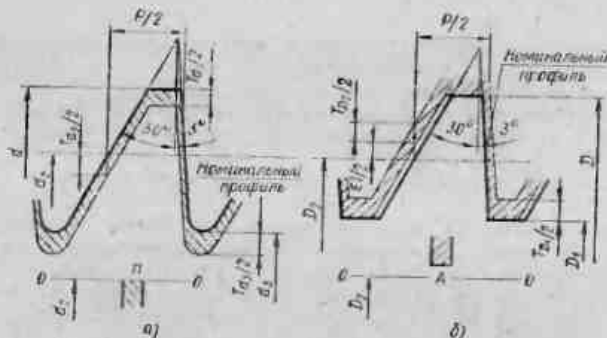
Расположение полей допусков упорной резьбы: а — наружной б — внутренней
